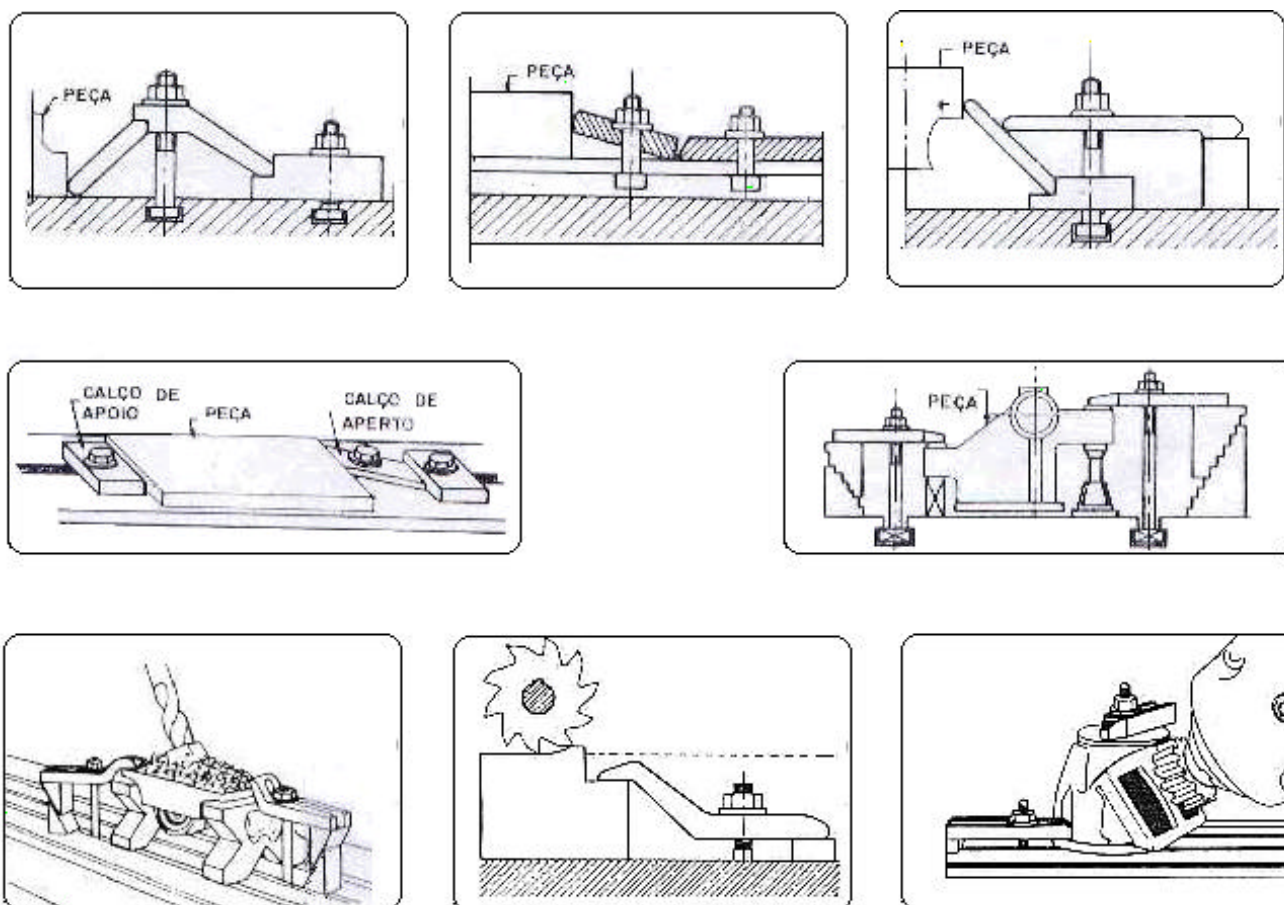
Tipos de fixações de peças diretamente na mesa de trabalho.
